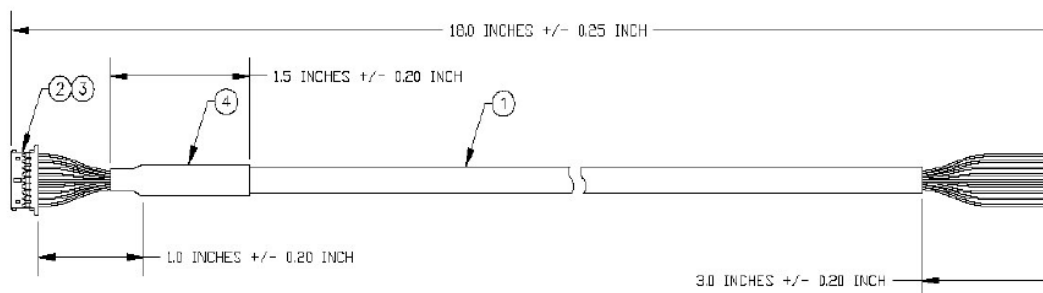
Dimensiones del cable de la brúixola/inclinòmetre TCM2.
